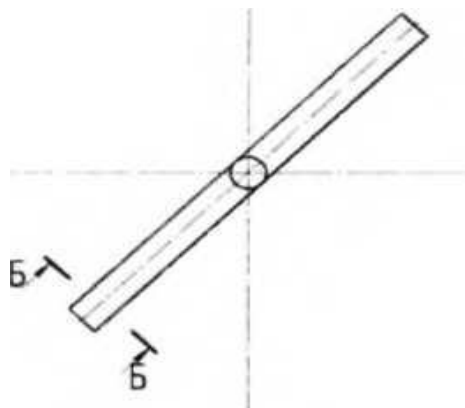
Променеподібний робочий орган, вид зверху - розріз Б-Б
